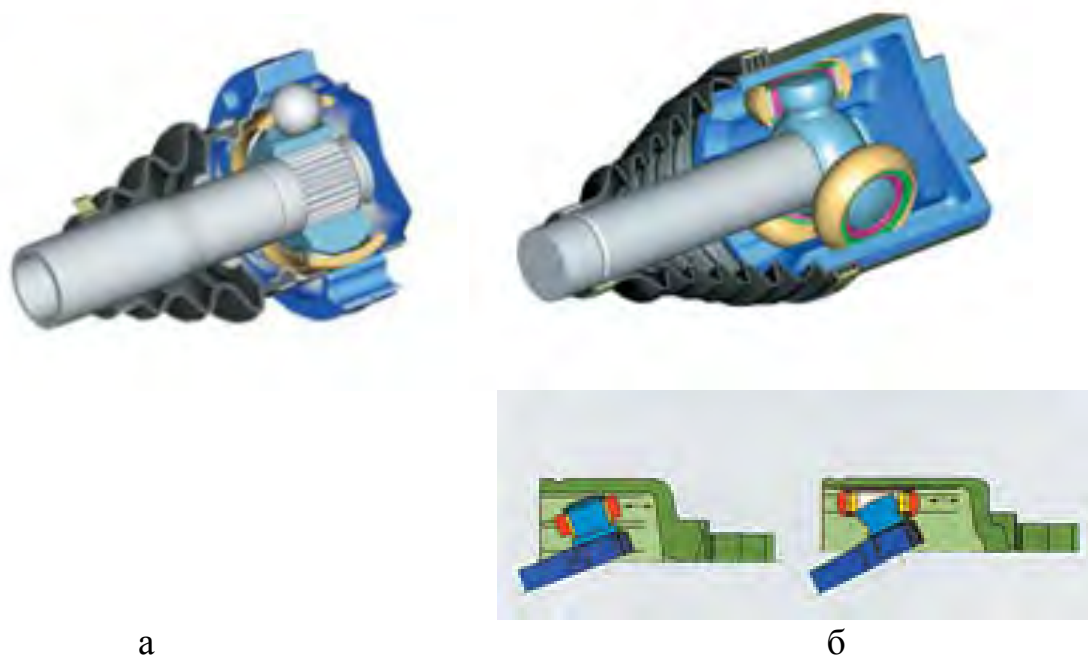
Шарнир типа VL (а) допускает осевое перемещение обойм; шарнир типа AAR (Angular Adjusted Roller) фирмы GKN Driveline (б)
